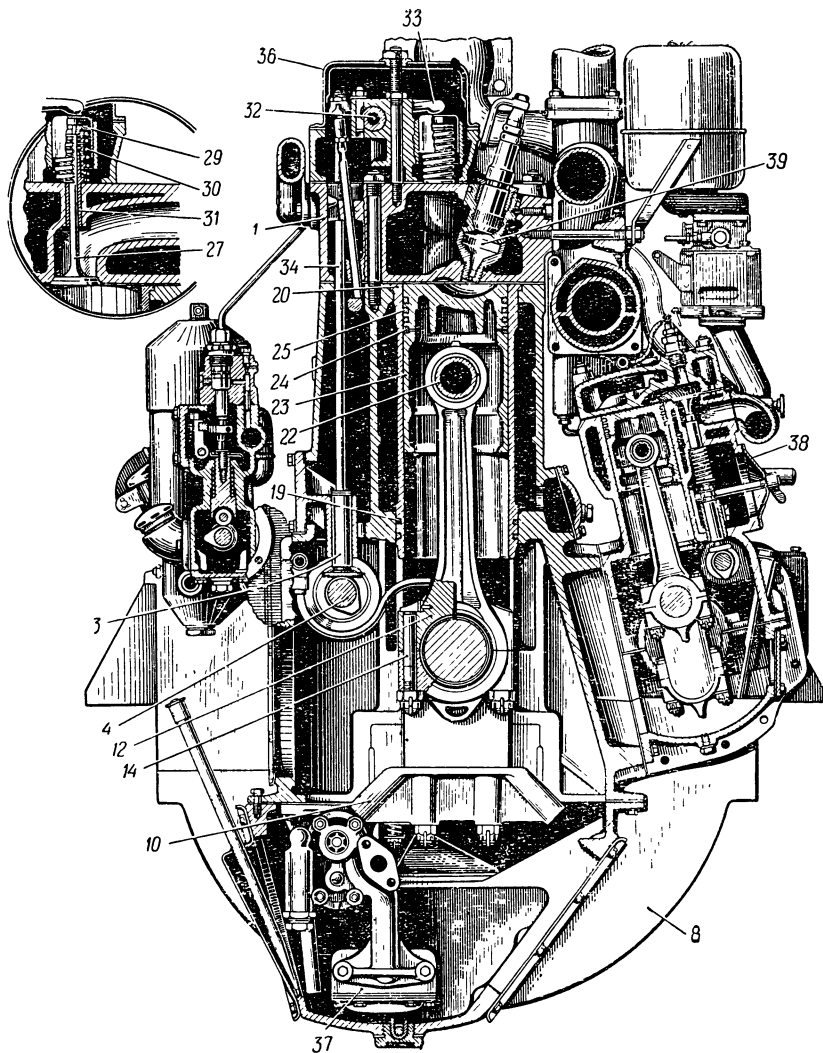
Четырехтактный дизель КДМ-46 (поперечный разрез):
